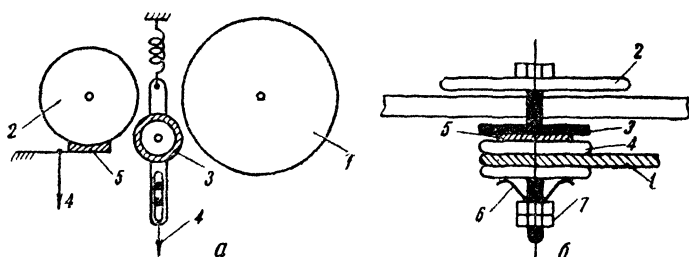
Варианты устройства узла левой кассеты: а) 1 — шкив двигателя; 2 — шкив на оси левой кассеты; 3 — паразитный обрезиненный ролик; 4 — управляющая тяга; 5 — подушка тормоза; б) 1 — ремень, связывающий фрикцион с двигателем; 2 — планшайба; 3 — верхняя металлическая половина фрикциона; 4 — нижняя текстолитовая часть фрикциона; 5 — суконная прокладка; 6 — пружина, прижимающая половины фрикциона друг к другу; 7 — гайка для регулировки сцепления
